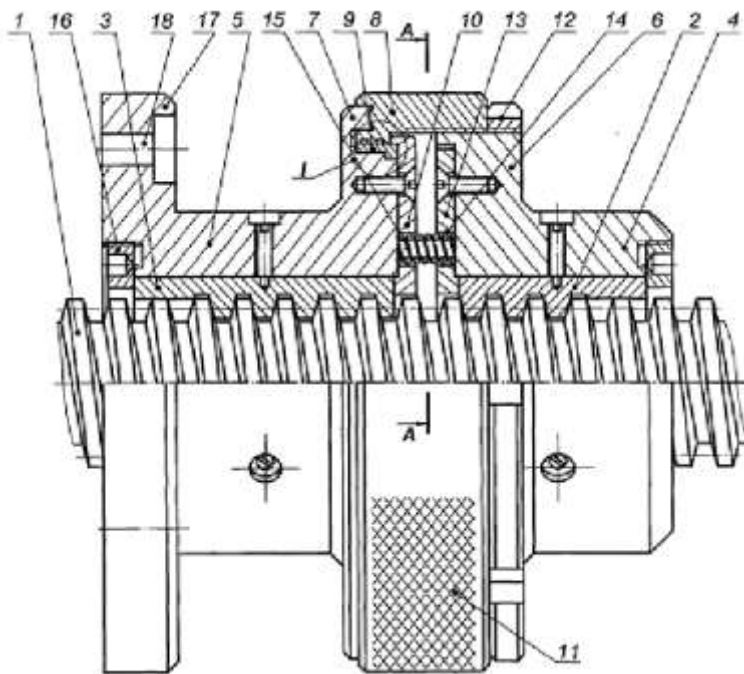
Пристрій для регулювання зазорів в передачі гвинт-гайка (Патент України № 53937).
